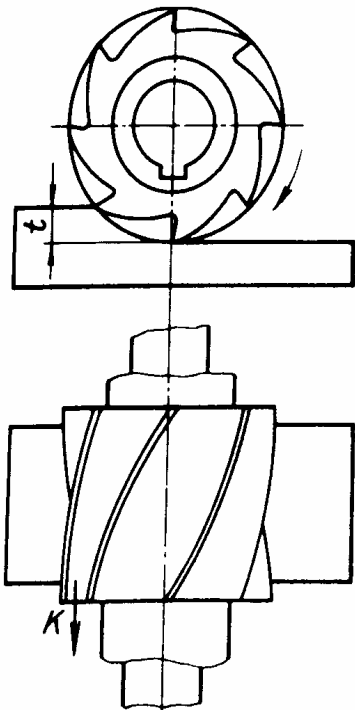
Схема фрезерування плоскої поверхні циліндричною фрезою: K – осьова складова сили різання; t – глибина різання
